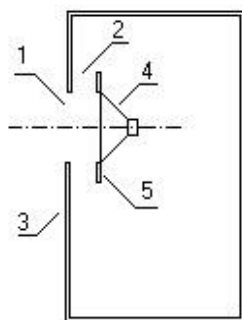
АС с головкой размещенной внутри корпуса, магнитной системой внутрь: 1 – отверстие акустической системы, 2 – воздушный зазор, 3 - передняя панель акустической системы, 4 – головка громкоговорителя, 5 – кольцевая панель громкоговорителя.
